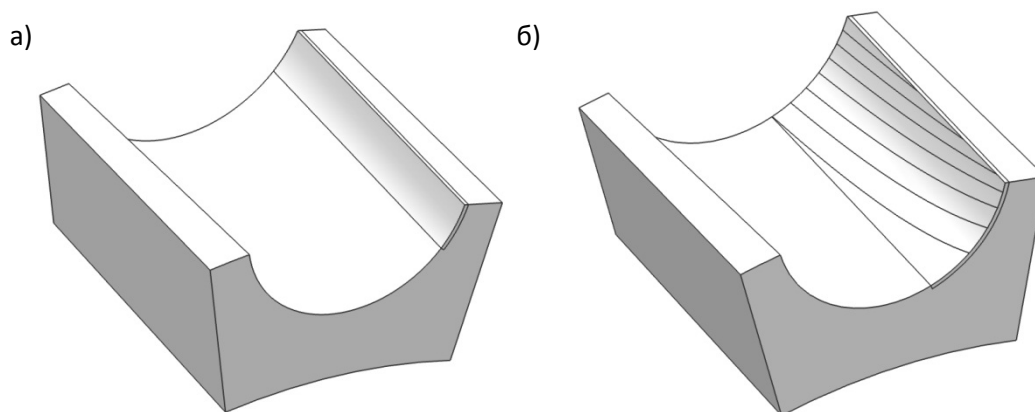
Модели зуба сателлита прецессионной передачи: а – теоретически точная поверхность зуба сателлита; б – приближенная поверхность зуба сателлита
